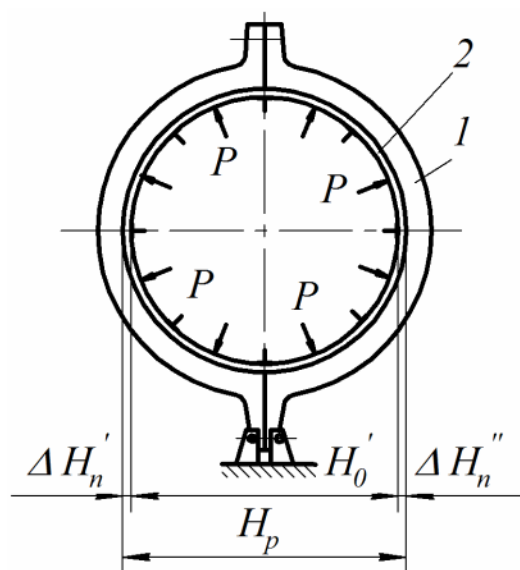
Принципова схема базування по зовнішній поверхні обшивки:
